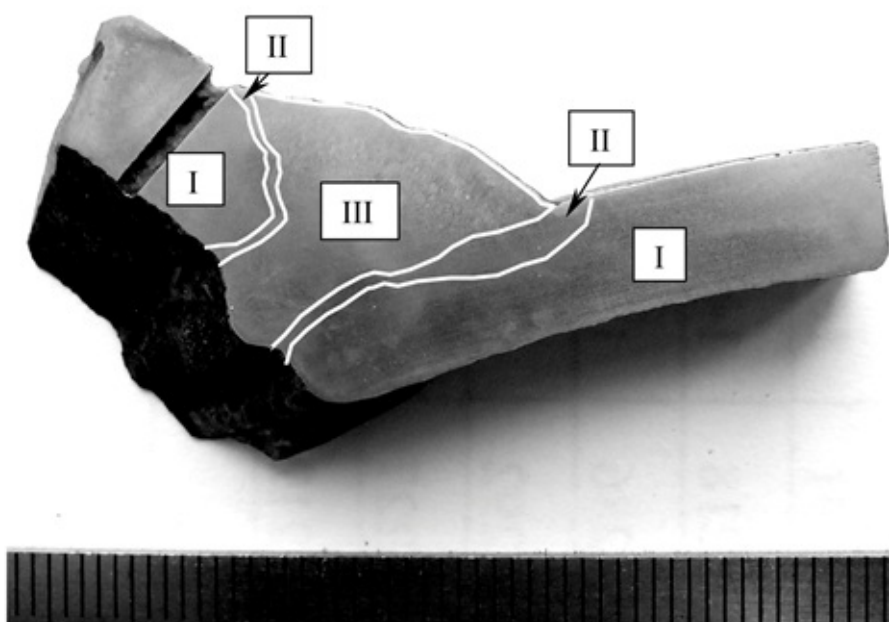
Темплет №1 с обозначением границ сварного шва (после травления):
